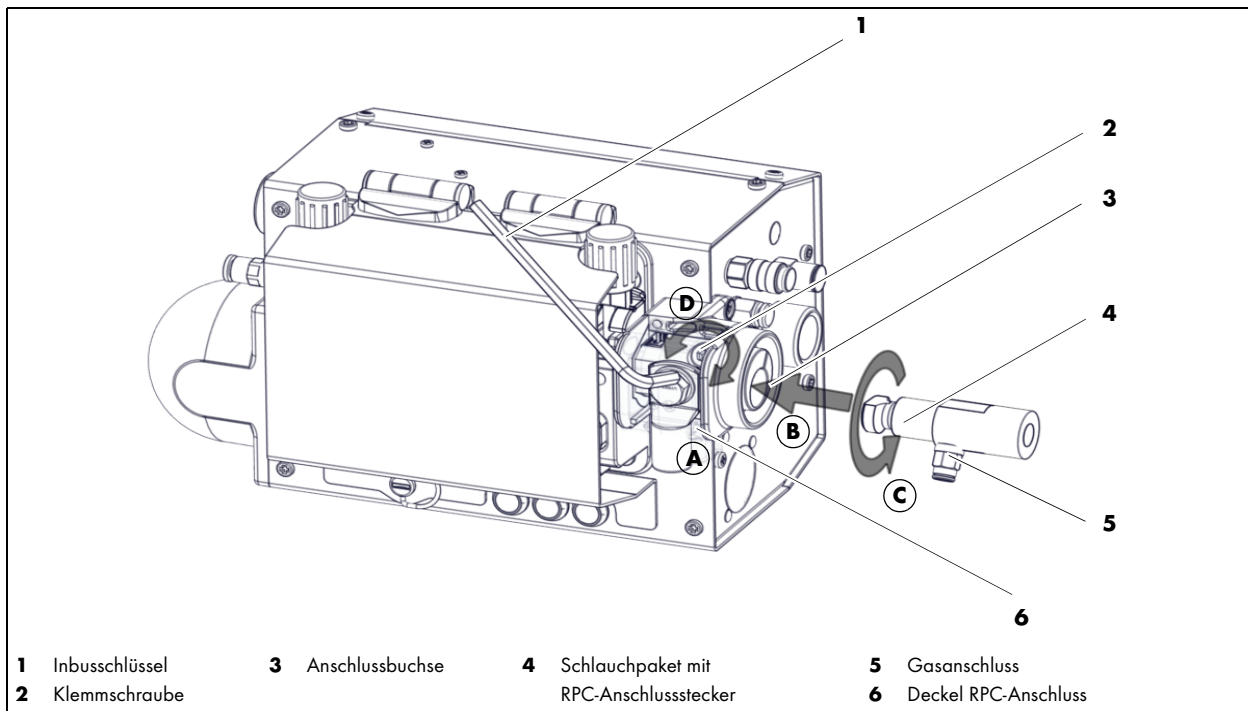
Schlauchpaket Schweißbrenner (RPC-Anschluss) iROB Feed 22 (Version mit Drahtvorschub rechts montiert)
